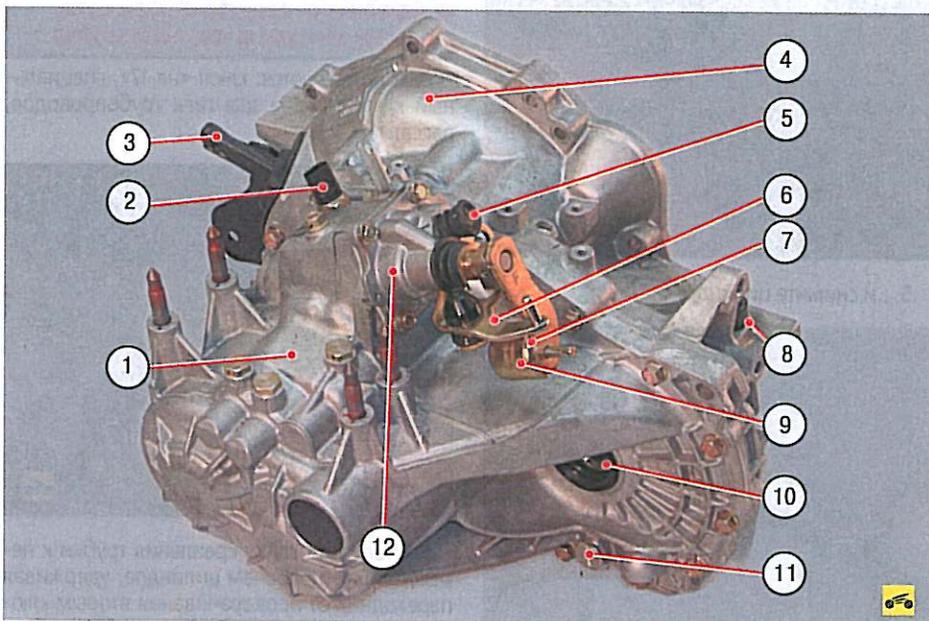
Механическая коробка передач: 1 – картер коробки передач; 2 – выключатель света заднего хода; 3 – вилка выключения сцепления; 4 – картер сцепления; 5 – сапун; 6 – рычаг выбора передач; 7 – рычаг переключения передач; 8 – датчик скорости; 9 – груз механизма переключения передач; 10 – сальник полуоси; 11 – пробка сливного отверстия; 12 – механизм переключения передач
